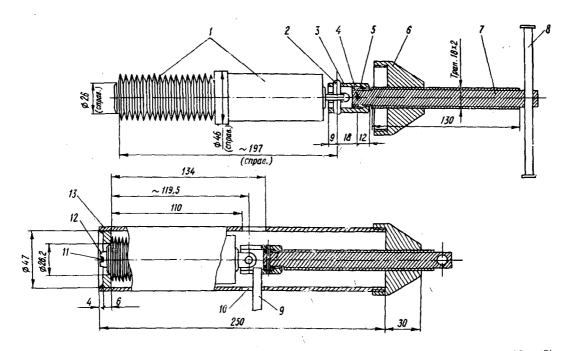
Приспособление для переборки пружинного амортизатора Ш4700-20 лыжонка (Ст. 45): 1- поршень амортизатора в сборе со штоками и пружинами; 2- палец \varnothing 6 мм; 3- втулка; 4- штифт \varnothing 2,5 мм; 5- гайка втулки; 6- крышка; 7- ходовой винт; 8- вороток; 9- пластина сечением 7×5 мм; 10- прорезь в цилиндре (овал 24×5 мм); 11- шайба контровочная Ш4700-33; 12- гайка Ш4700-31; 13- цилиндр приспособления
